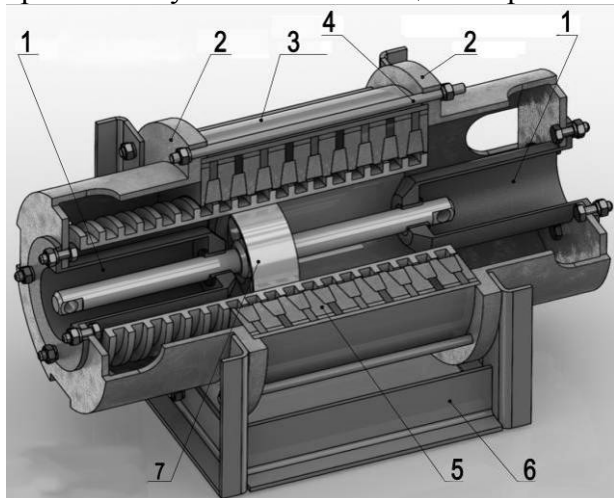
Общий вид экспериментальной линейной электрической машины: 1- стакан направляющий; 2 – фланец; 3- кожух; 4 – шпилька; 5 – статор; 6 – опорный каркас; 7 – подвижный элемент
